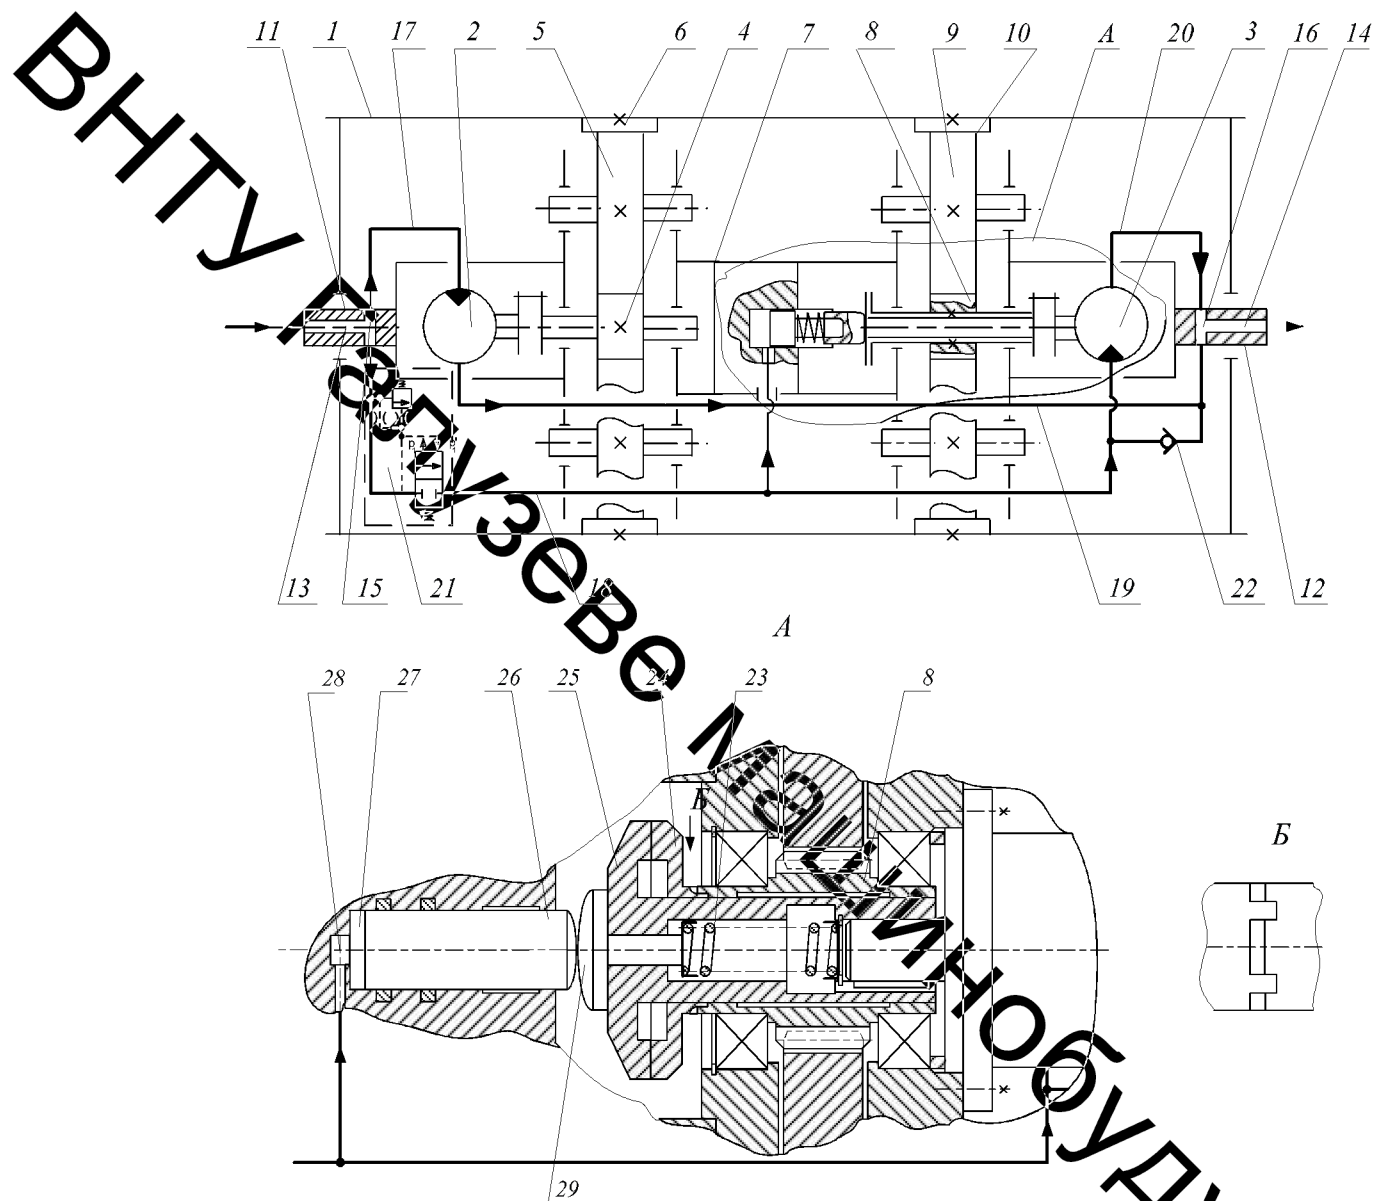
Конструктивна схема керованого гідравлічного мотор-барабана
